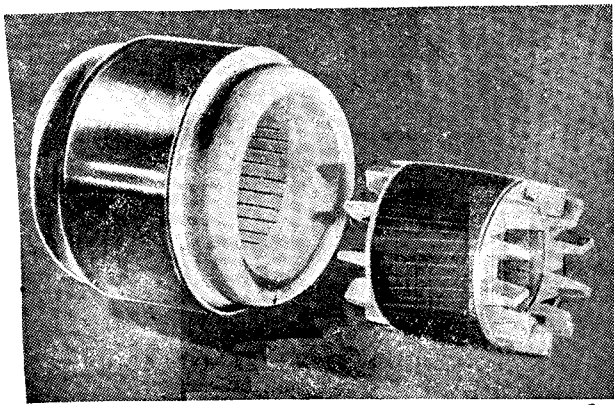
Двигатель с обмазкой лобовых частей обмотки статора
